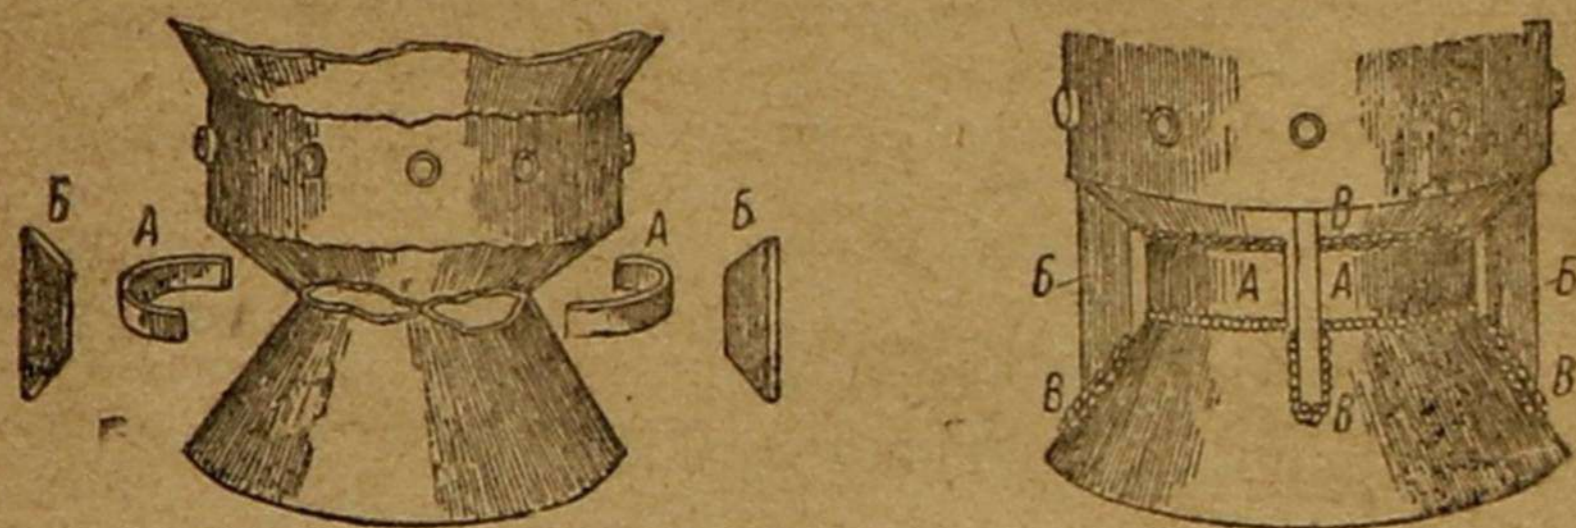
Полукольца и упорки для ремонта топливника: А—полукольца; Б—упорки; В—сварочные швы
